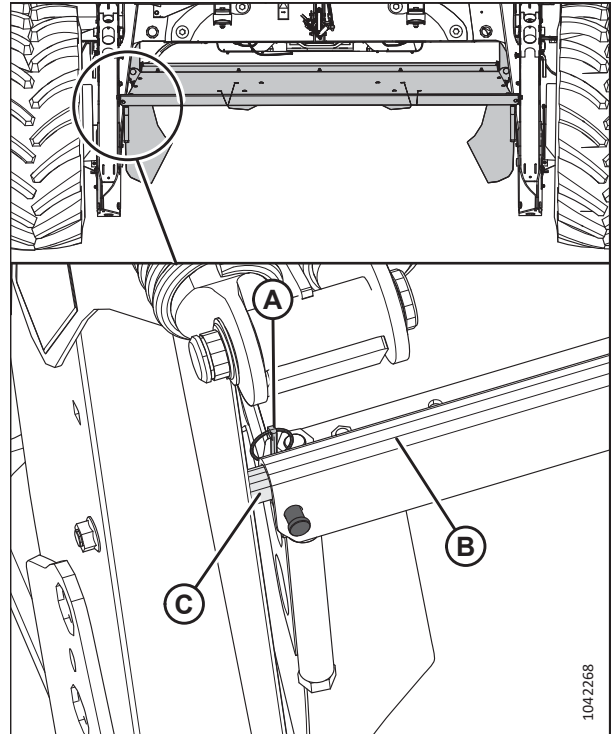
Формовочный щиток, прикрепленный к передней части стоек косилки
